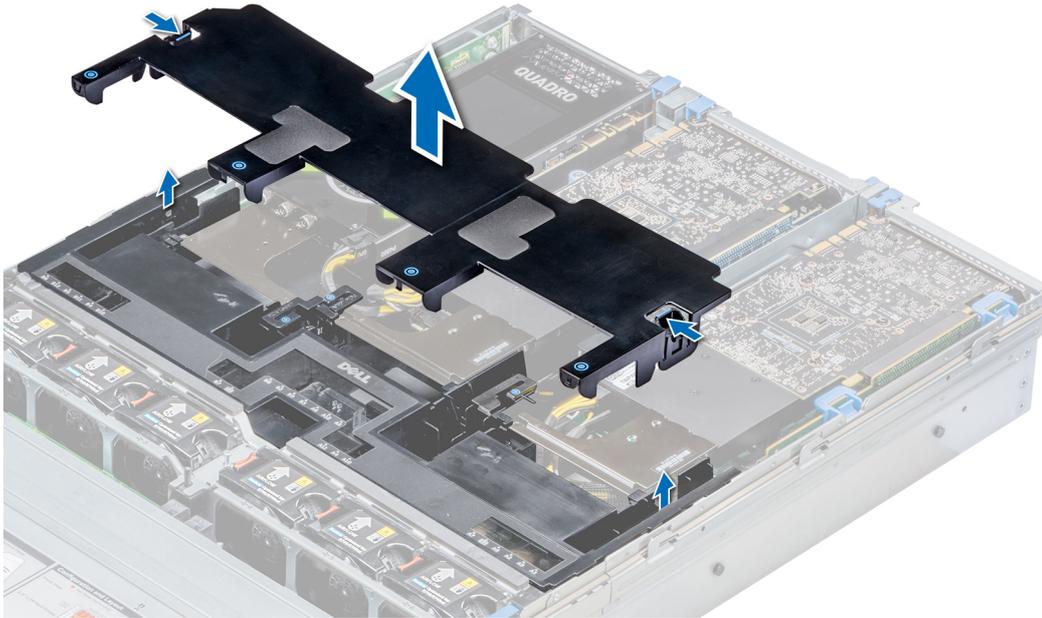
Entfernen der oberen Abdeckung des Kühlgehäuses
